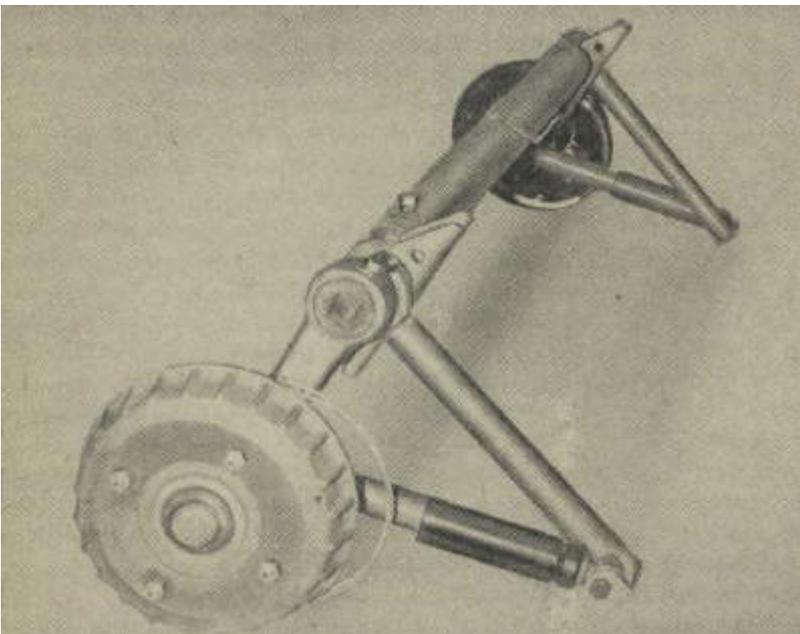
Komplette 650-kg-Campinganhängerachse mit Schwinghebeln und Stoßdämpfern
